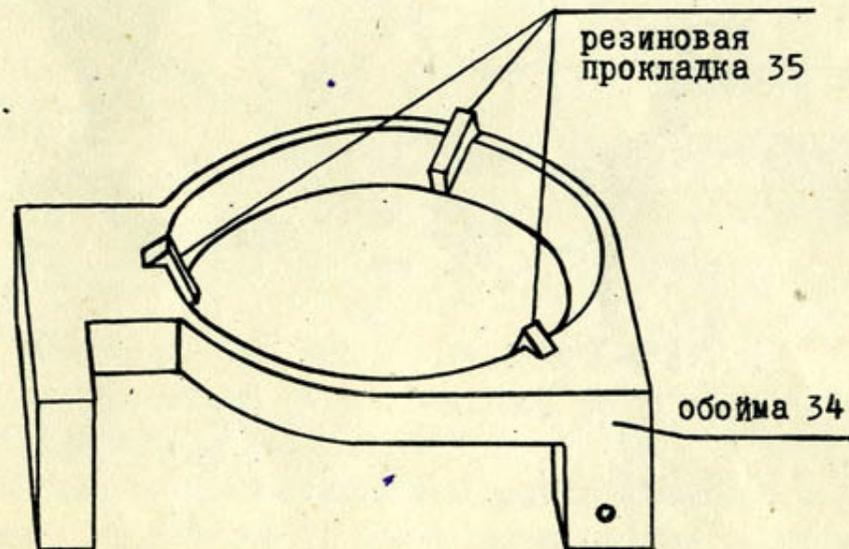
Установка резиновых прокладок на обойму крепления кинескопа
